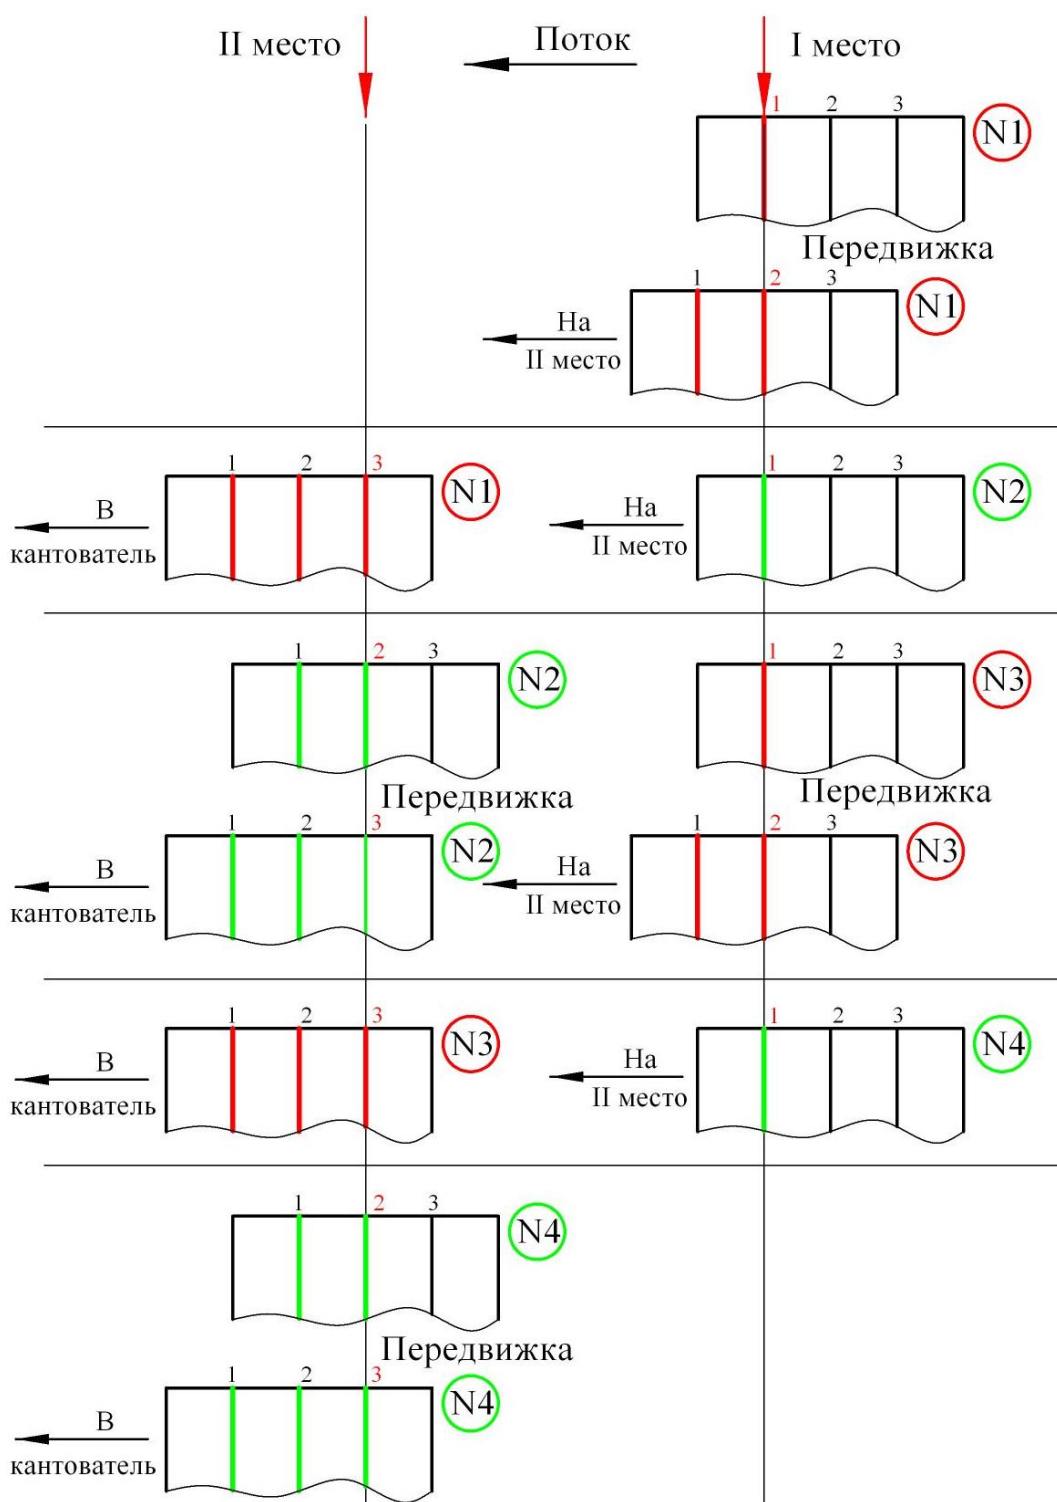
Схема сварки на двухместном стенде трех стыковых листовых полотнищ:
